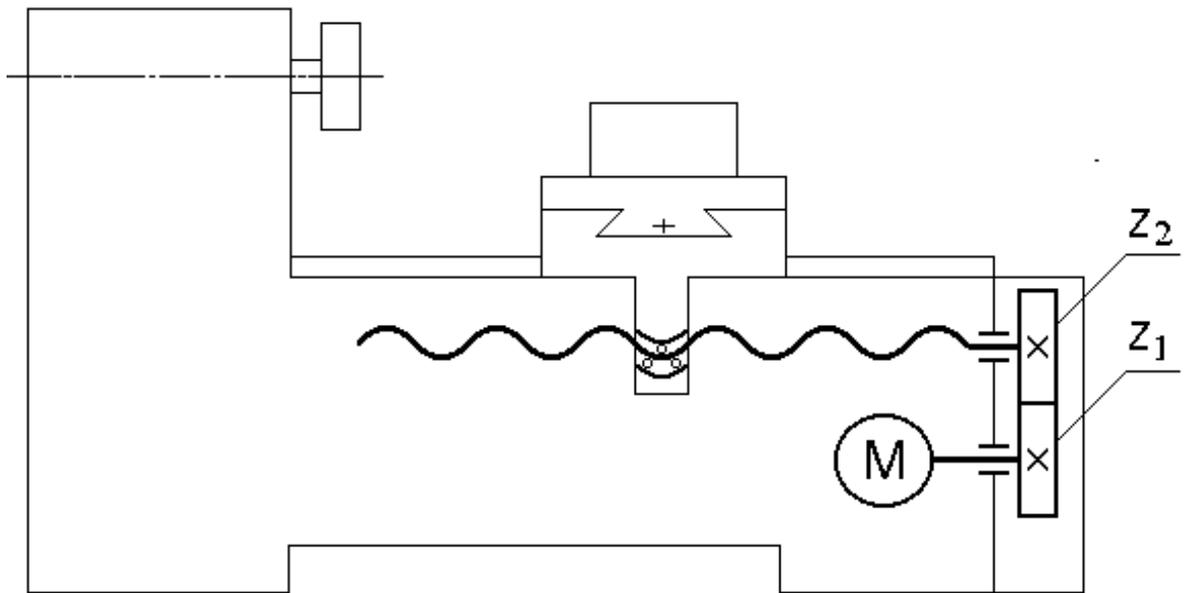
Кинематическая схема привода подач станка с ЧПУ.
